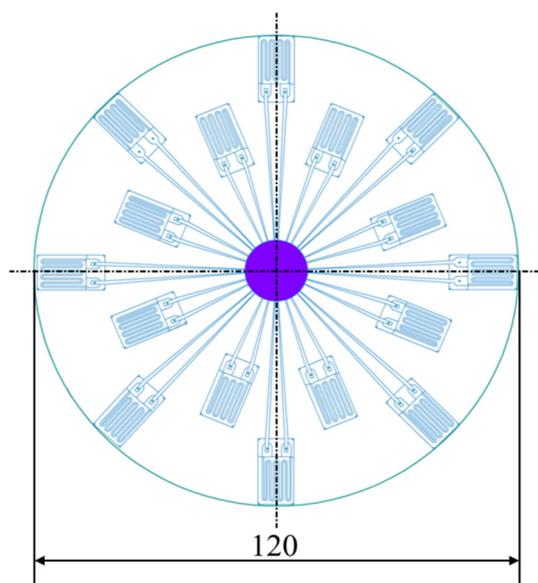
Расположение тензорезисторов на рабочей поверхности поршня
